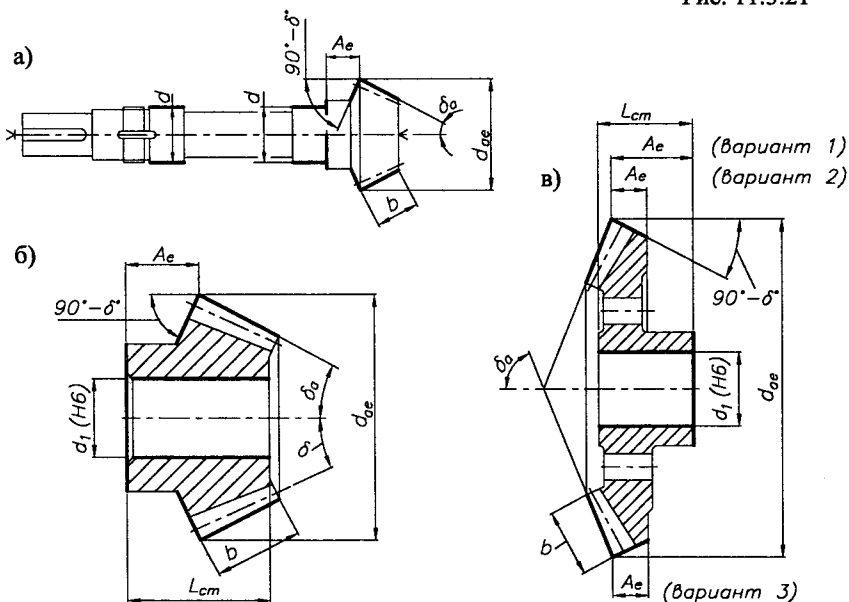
Размеры, требующие указания точности, для заготовок: а) вал-шестерни; б) шестерни; в) колеса
